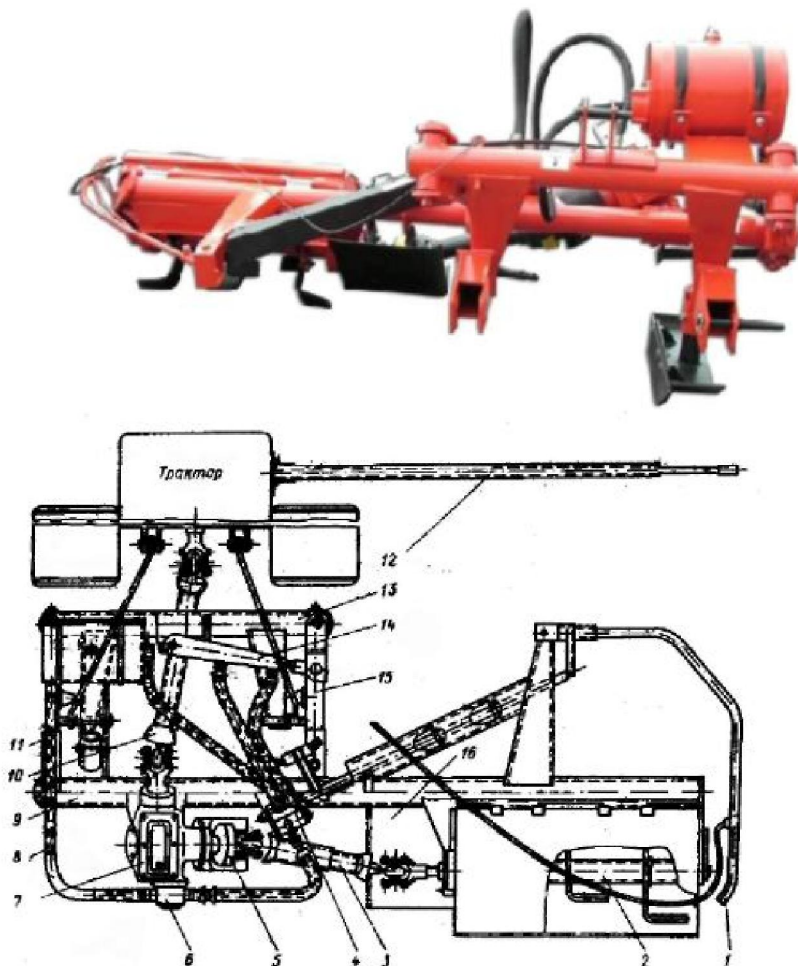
Загальний вигляд і схема фрези садової ФА-0,76: 1 - щуп; 2 - фрезерний барабан (ротор); 3, 10 - вали карданні; 4 - гідро-розподільувач; 5 - запобіжна муфта; 6 - насос; 7 - конічний редуктор; 8 - шланги; 9 - несучий брус; 11, 15 - ланки паралелограма повздовжні; 12 - маркер; 13 - брус передній; 14 - гідроциліндр; 16 - полозки.
